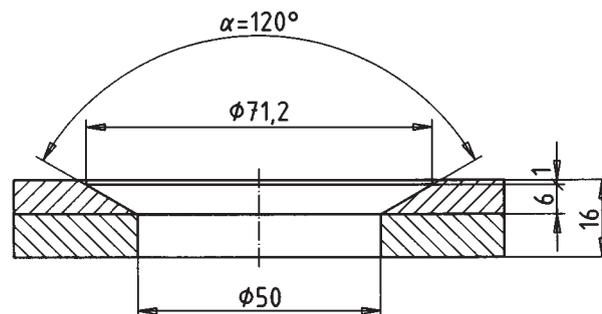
Prüfllehre für die Prüfung der Ablaufventile für Badewannen
